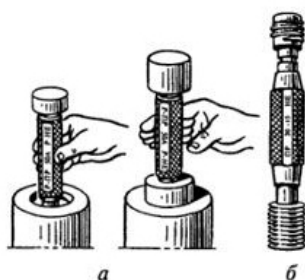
Калибр пробки: а – гладкая предельная; б – резьбовая двусторонняя
